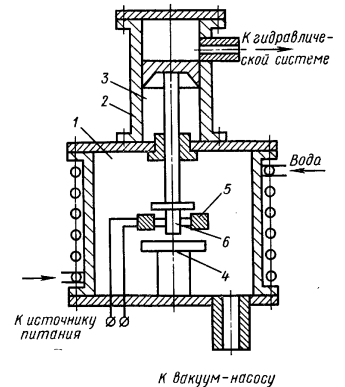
Принципиальная схема установки для диффузионной сварки в вакууме:
